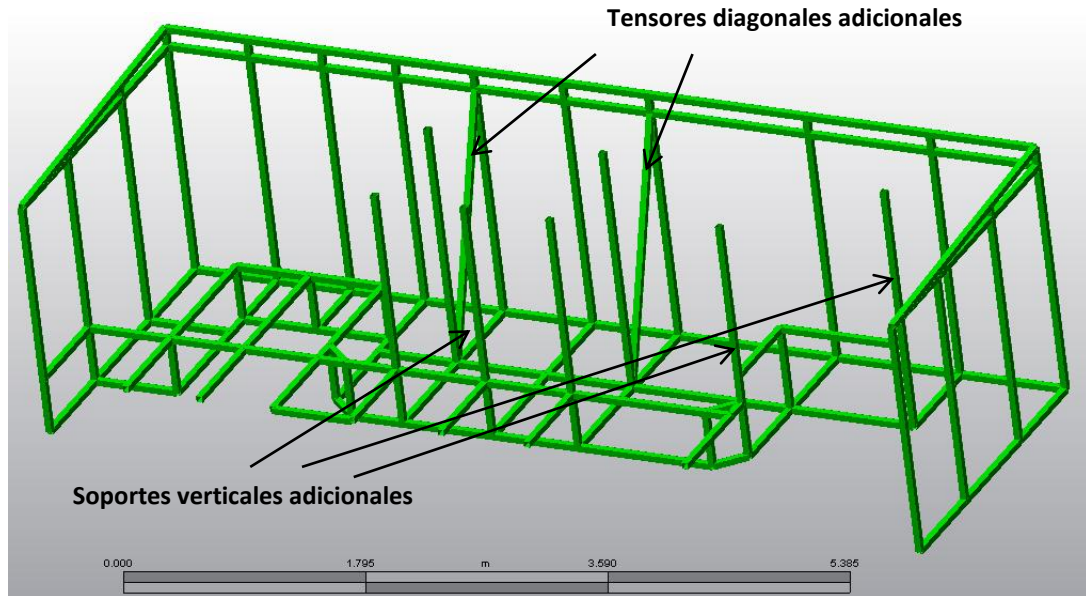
Refuerzos verticales y diagonales en la Planta Alta
